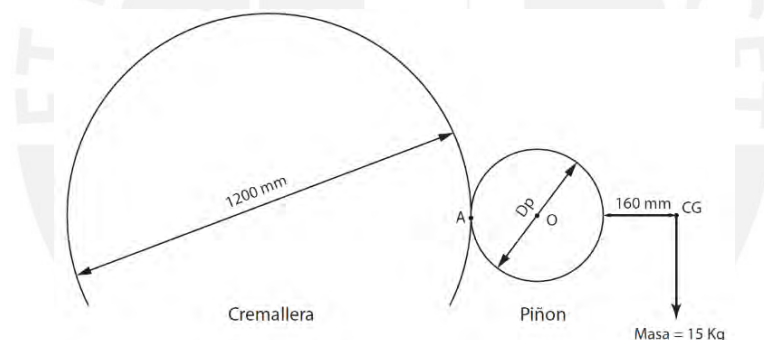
Centro de gravedad del tractor soldador sobre la cremallera
